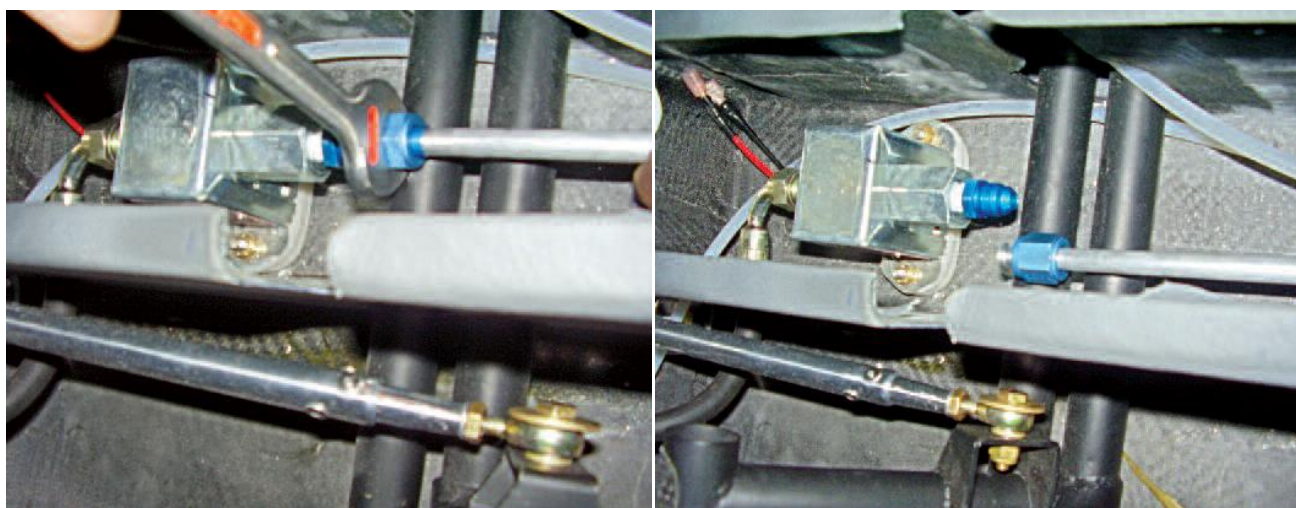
Tubo AA-28-20-400-44 e Bomba elétrica de Combustível
